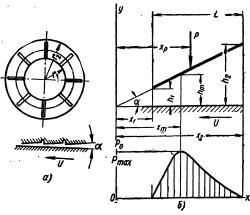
Упорный подшинник с неподвижными сегментами: а - подпятник; б - положение сегмента в смазочном слое
